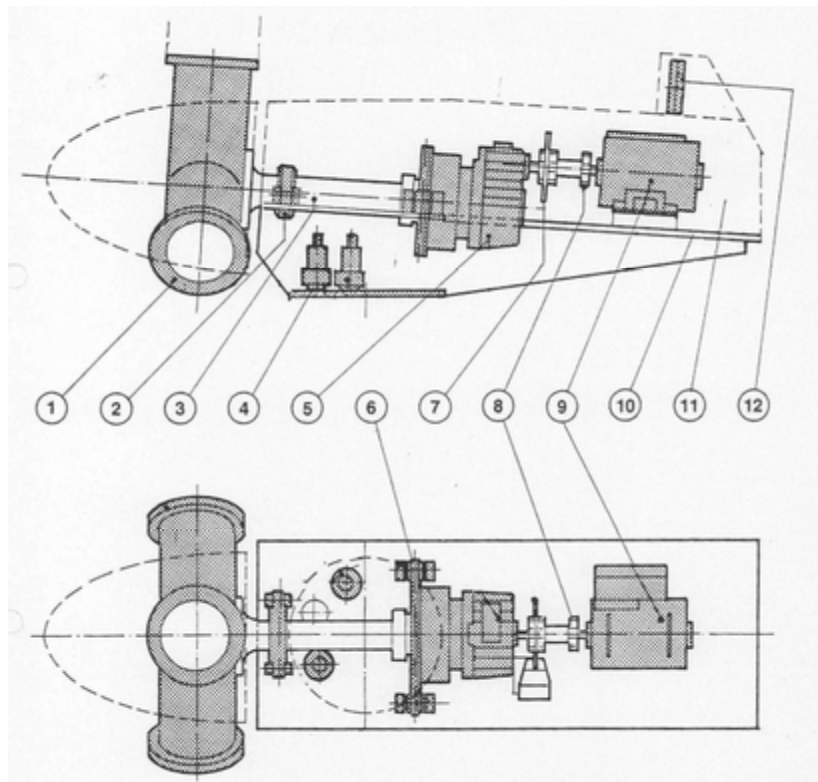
Устройство ВЭС Micon M1500: 1 – ротор; 2 – главный подшипник; 3 – главный вал; 4 – поворотный механизм; 5 – редуктор; 6 – крепление редуктора; 7 – тормоз
